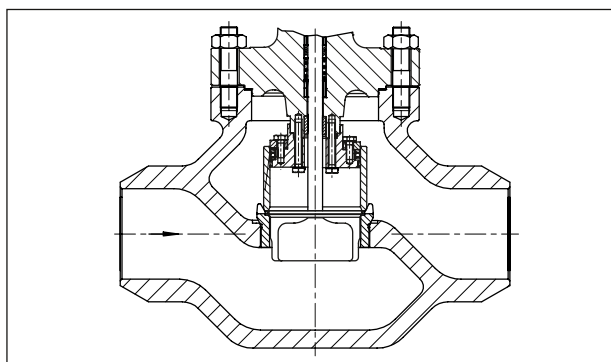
Válvula Tipo 3251/3251-AM com extremidades para soldar e obturador equilibrado
